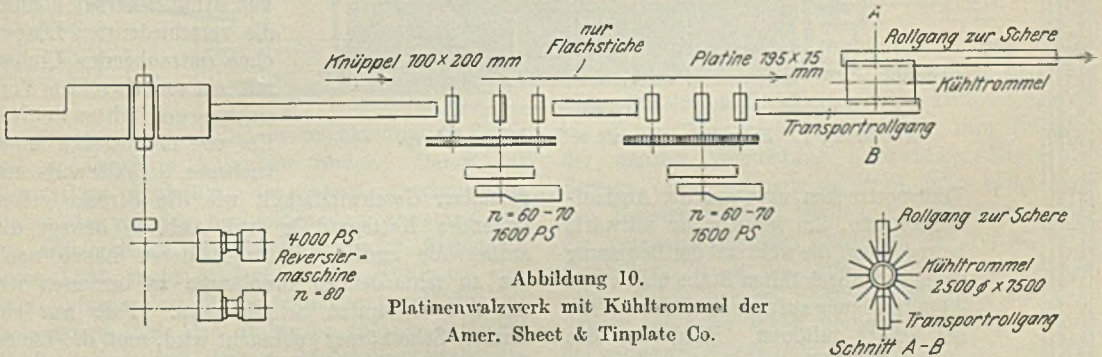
Platinenwalzwerk mit Kühltrömmel der Amer. Sheet & Tinplate Co.
